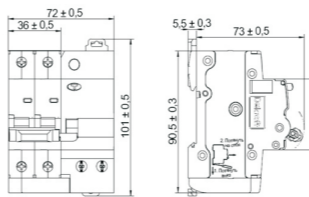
Габаритные и установочные размеры УЗДП 25-63 А
